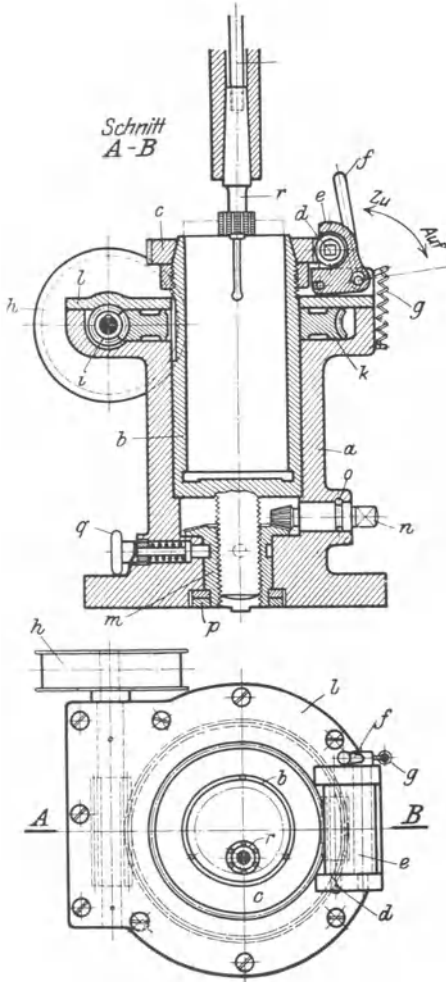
Senkrecht-Gewinde-Fräsvorrichtung.
